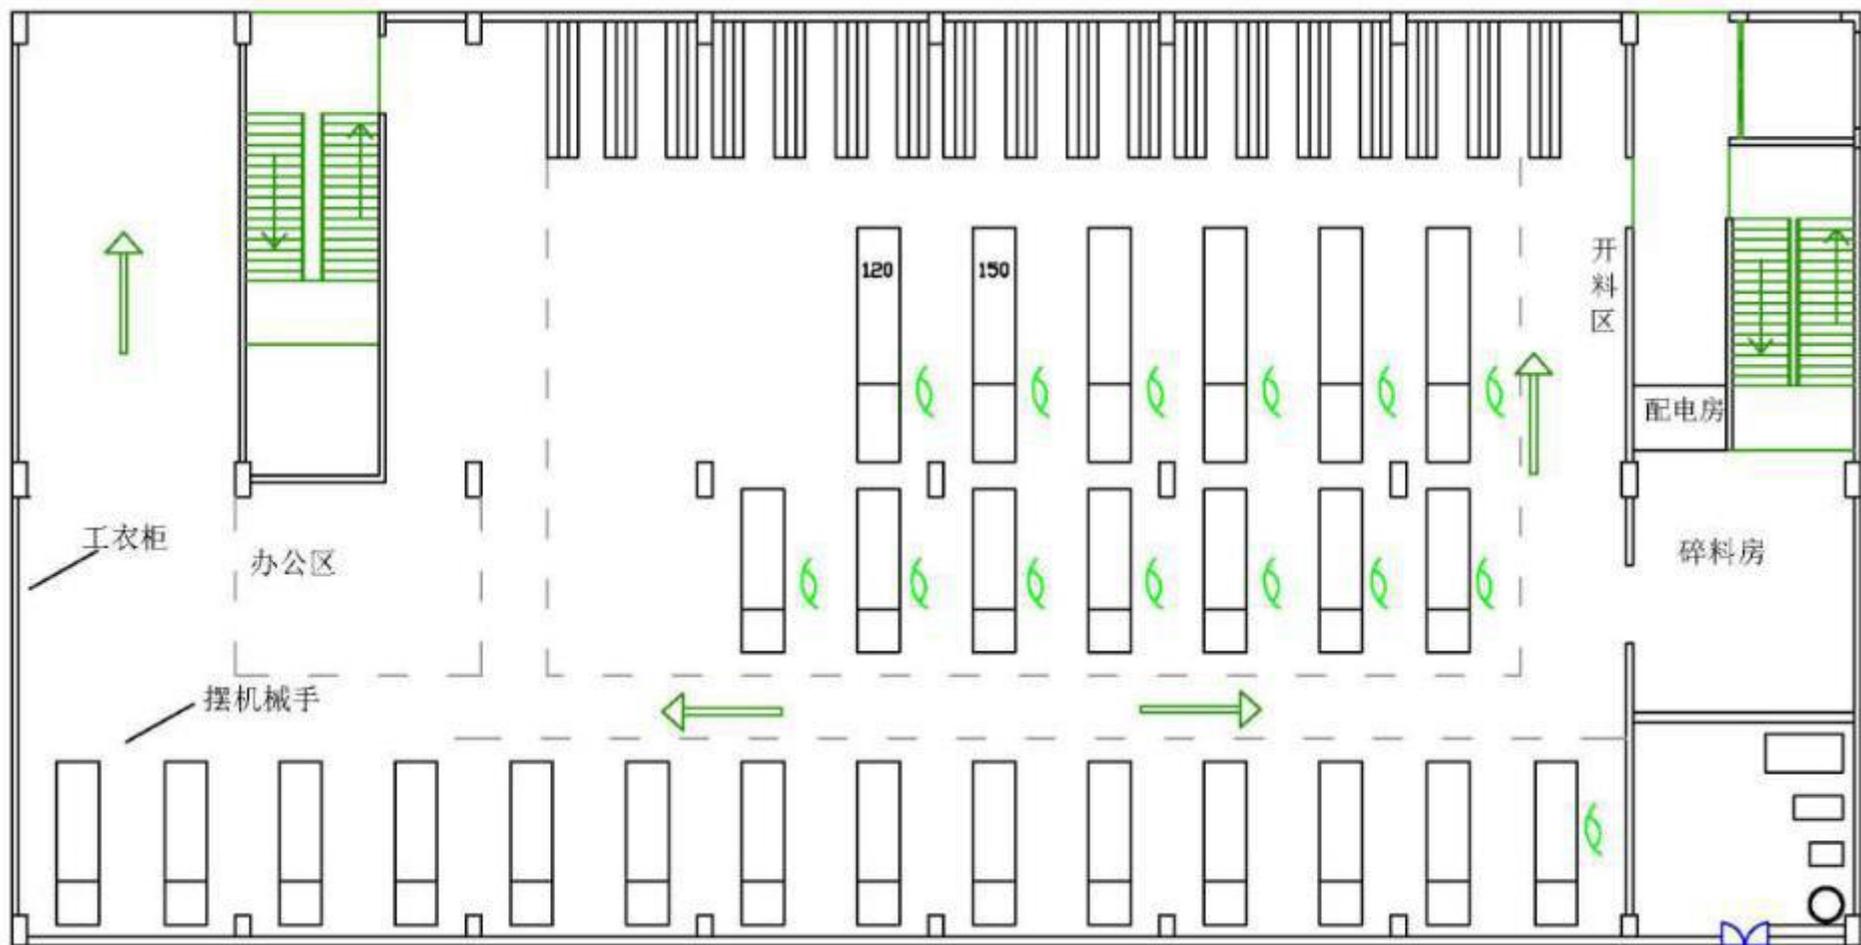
厂房平面布置图（注塑车间，E 栋一层）
